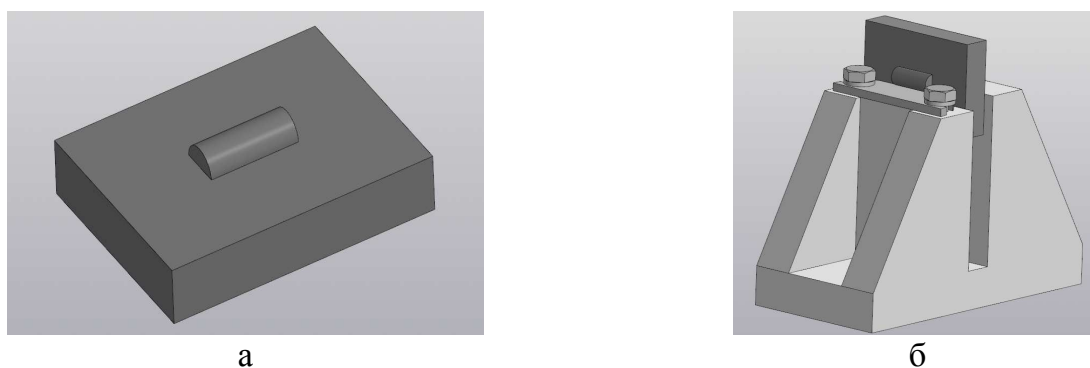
а) образец для испытаний на срез, б) образец, установленный в оснастку для испытания на срез
